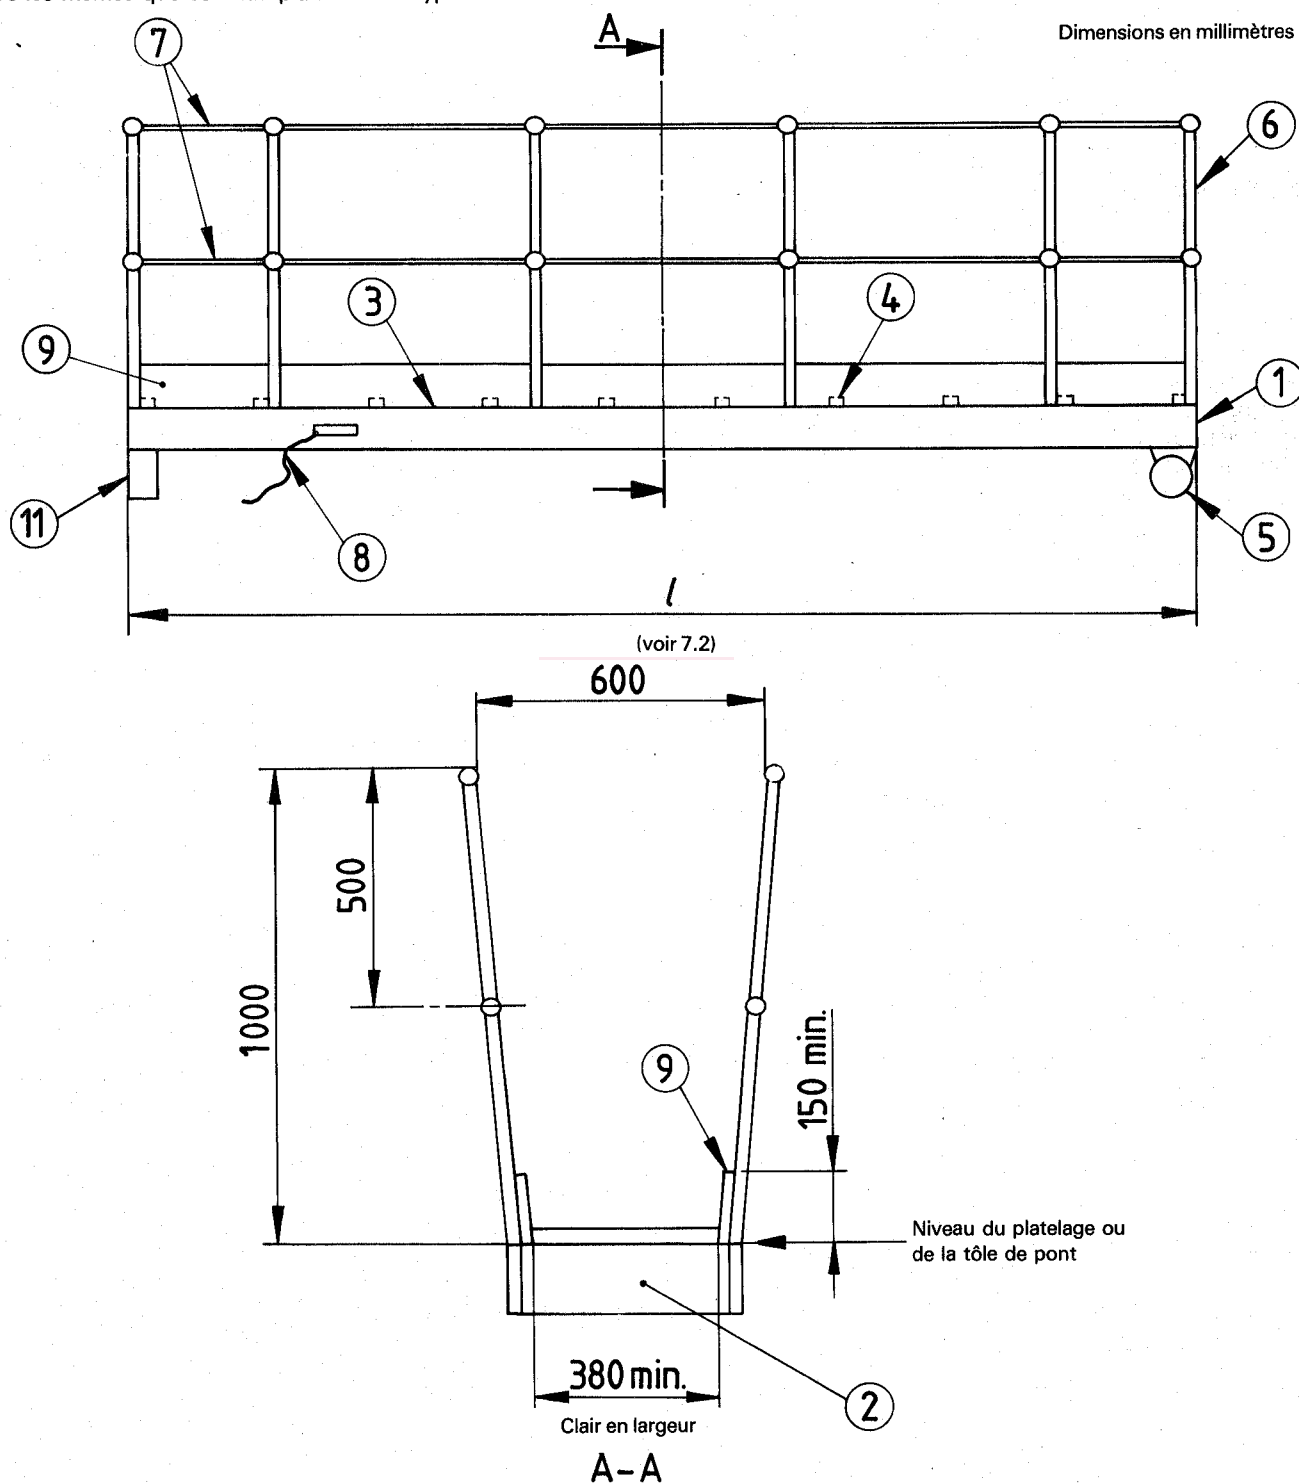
Disposition générale d'un planchon de type B (voir le tableau pour les numéros de référence)
